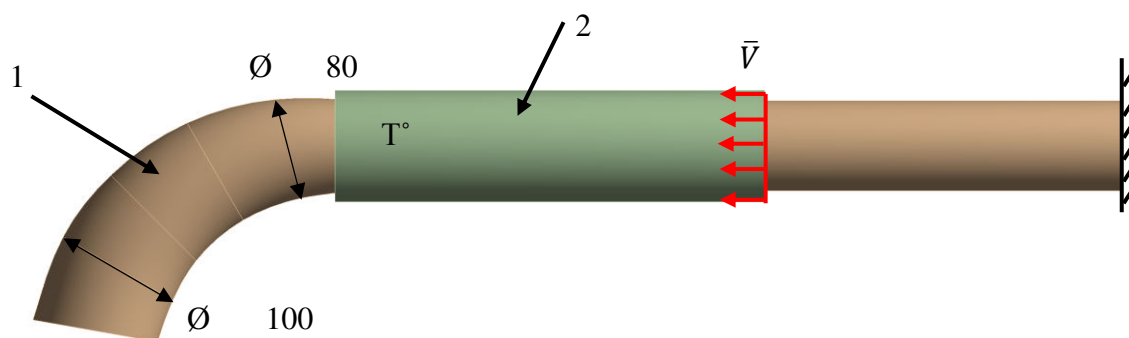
Постановка задачи; 1 – рогаобразный сердечник, 2 – заготовка
